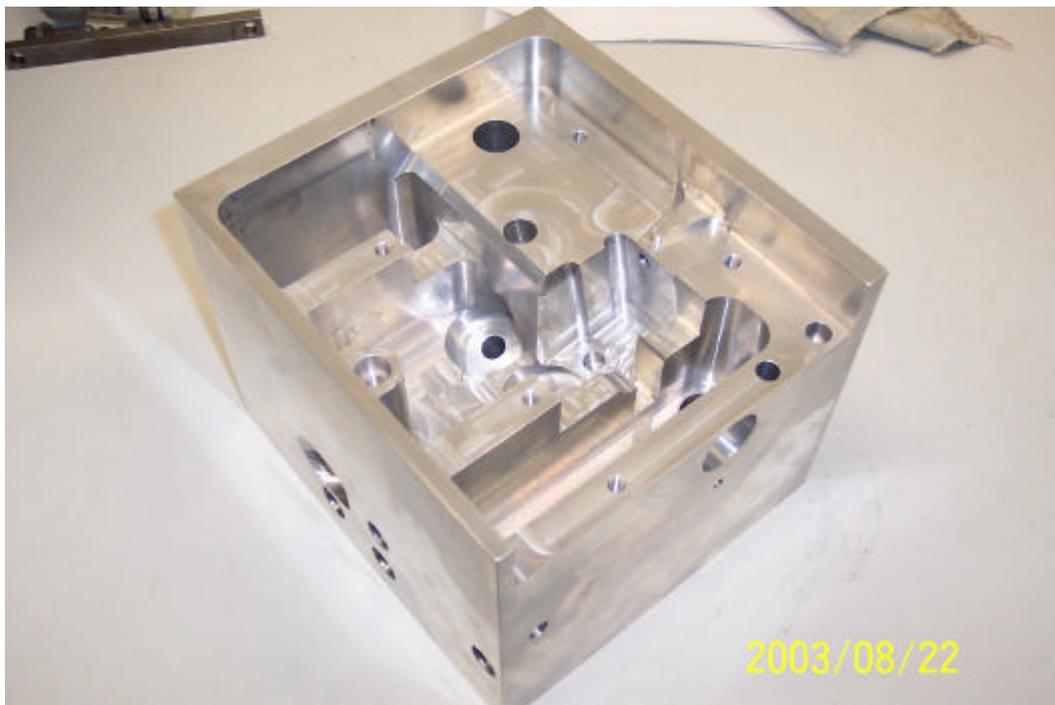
Zylinderkopfprototyp aus Aluminium gefräst
